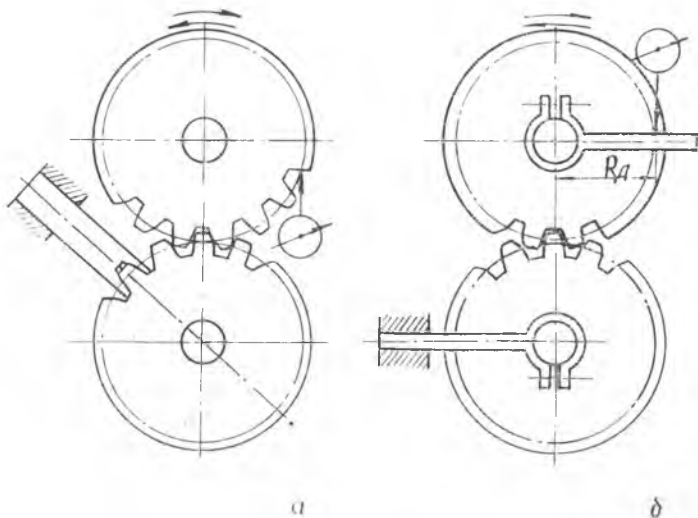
Схема контроля бокового зазора в зацеплении зубчатых колес
